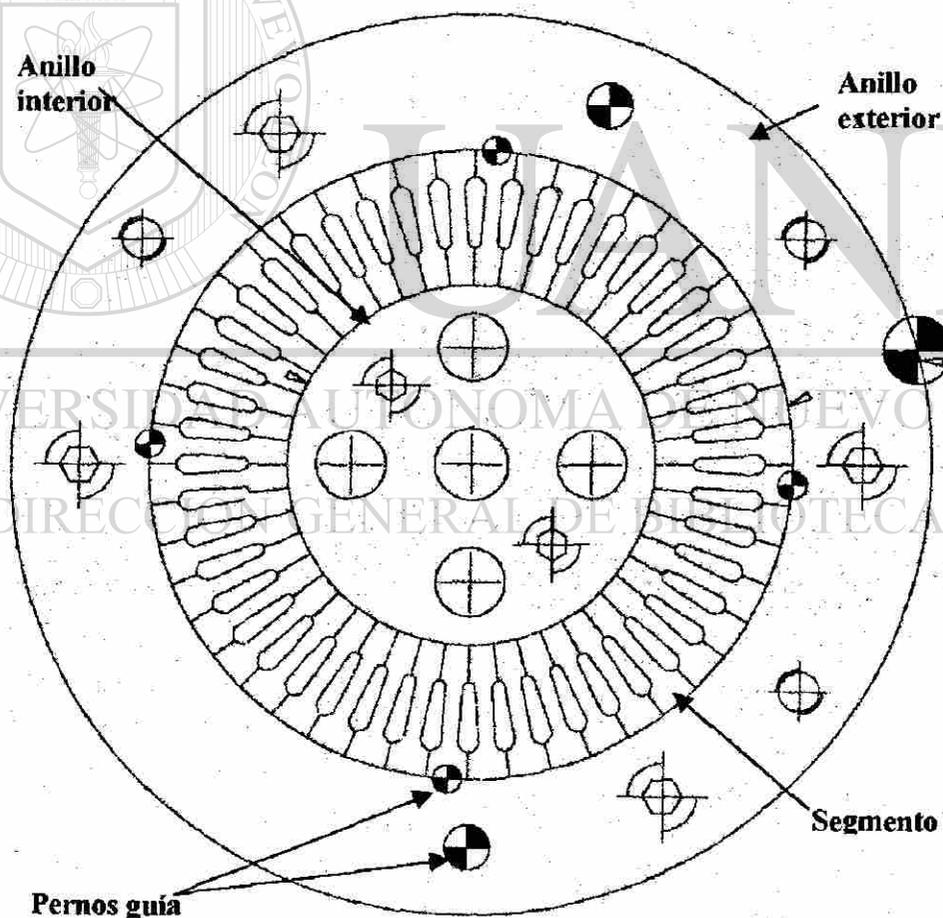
Ensamblaje de matices para el punzonado de rotor
